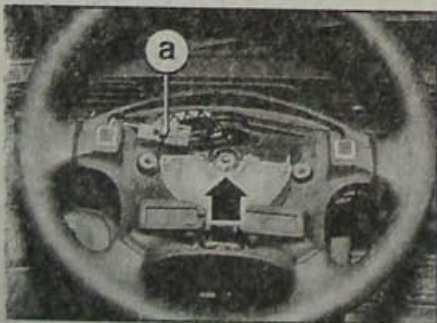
Расположение гайки крепления рулевого колеса с подушкой безопасности;
